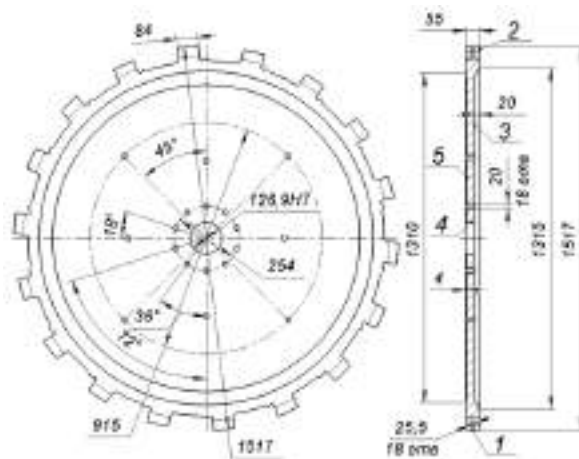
Фрагмент рабочего чертежа детали «Пильный диск»
